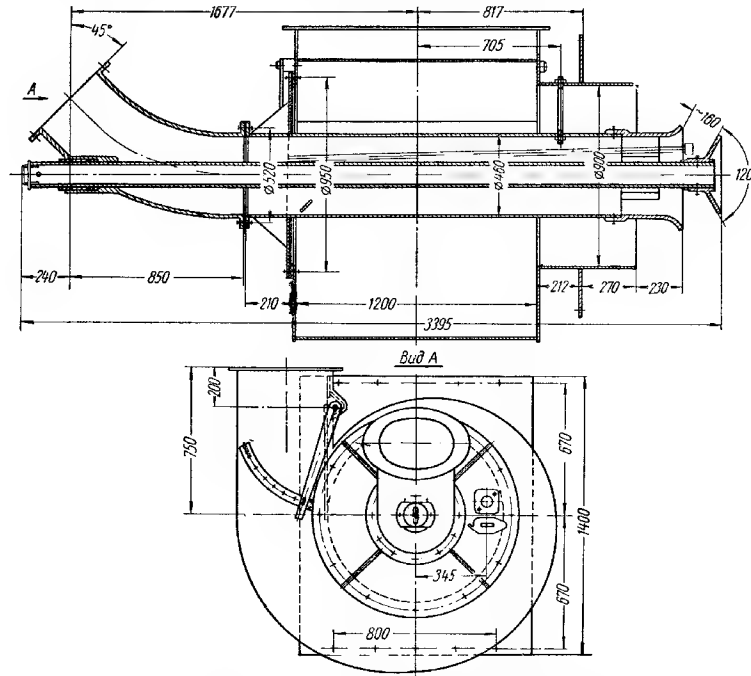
Круглая горелка конструкции ОРГРЭС
